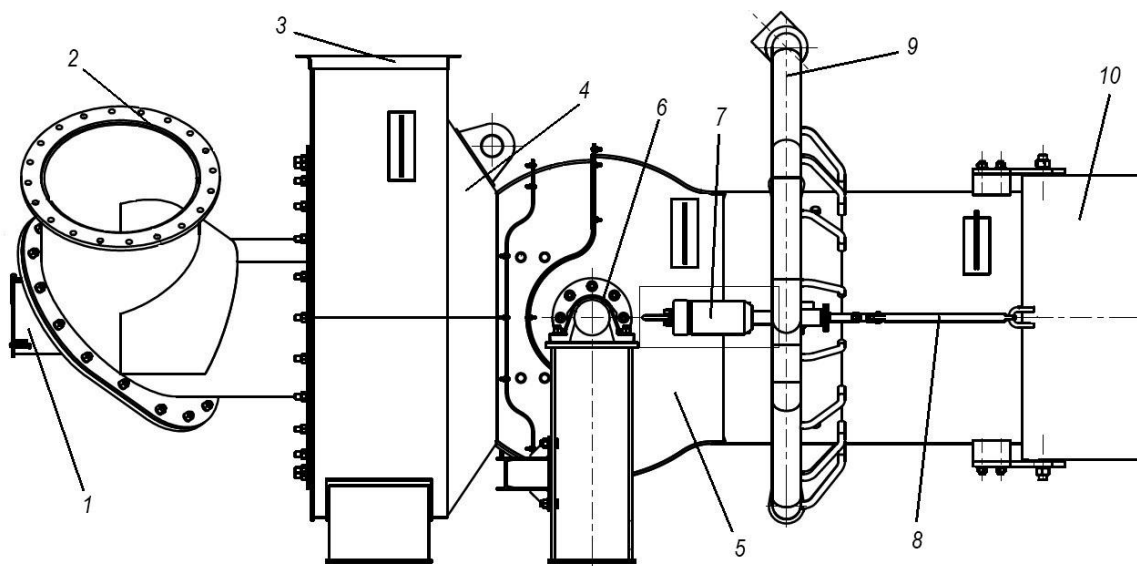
Вид горелки сбоку (1, 2 – входные патрубки центрального канала и аэросмеси; 3 – входной короб вторичного воздуха; 4, 5 – статичная и поворотная части горелки; 6 – подшипник поворотного вала горелки; 7 – механизм электрический прямоходный (МЭП); 8 – тяга от МЭП к поворотной насадке; 9 – газовый коллектор; 10 – выходная насадка для горизонтального поворота)
